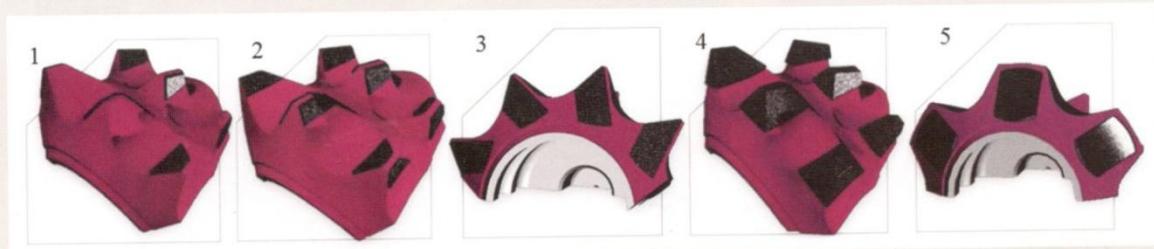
Схемы армирования фрезерованных зубьев: 1 – наплавляется только одна грань; 2 – наплавляется набегающая грань и часть сбегающей грани; 3 – наплавляются полностью торцы Г- и Т-образных зубьев; 4 – Т-усиленная объемная наплавка зубьев; 5 – W-усиленный периферийный (калибрующий) ряд.
